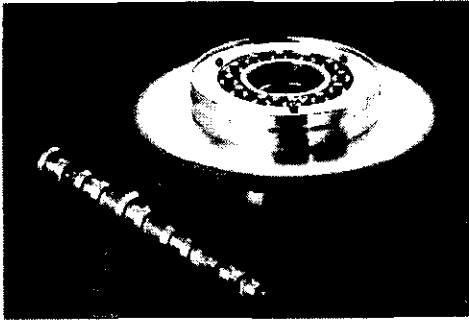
Cam shaft 연삭용 비트리화이드본드 CBN 휠
